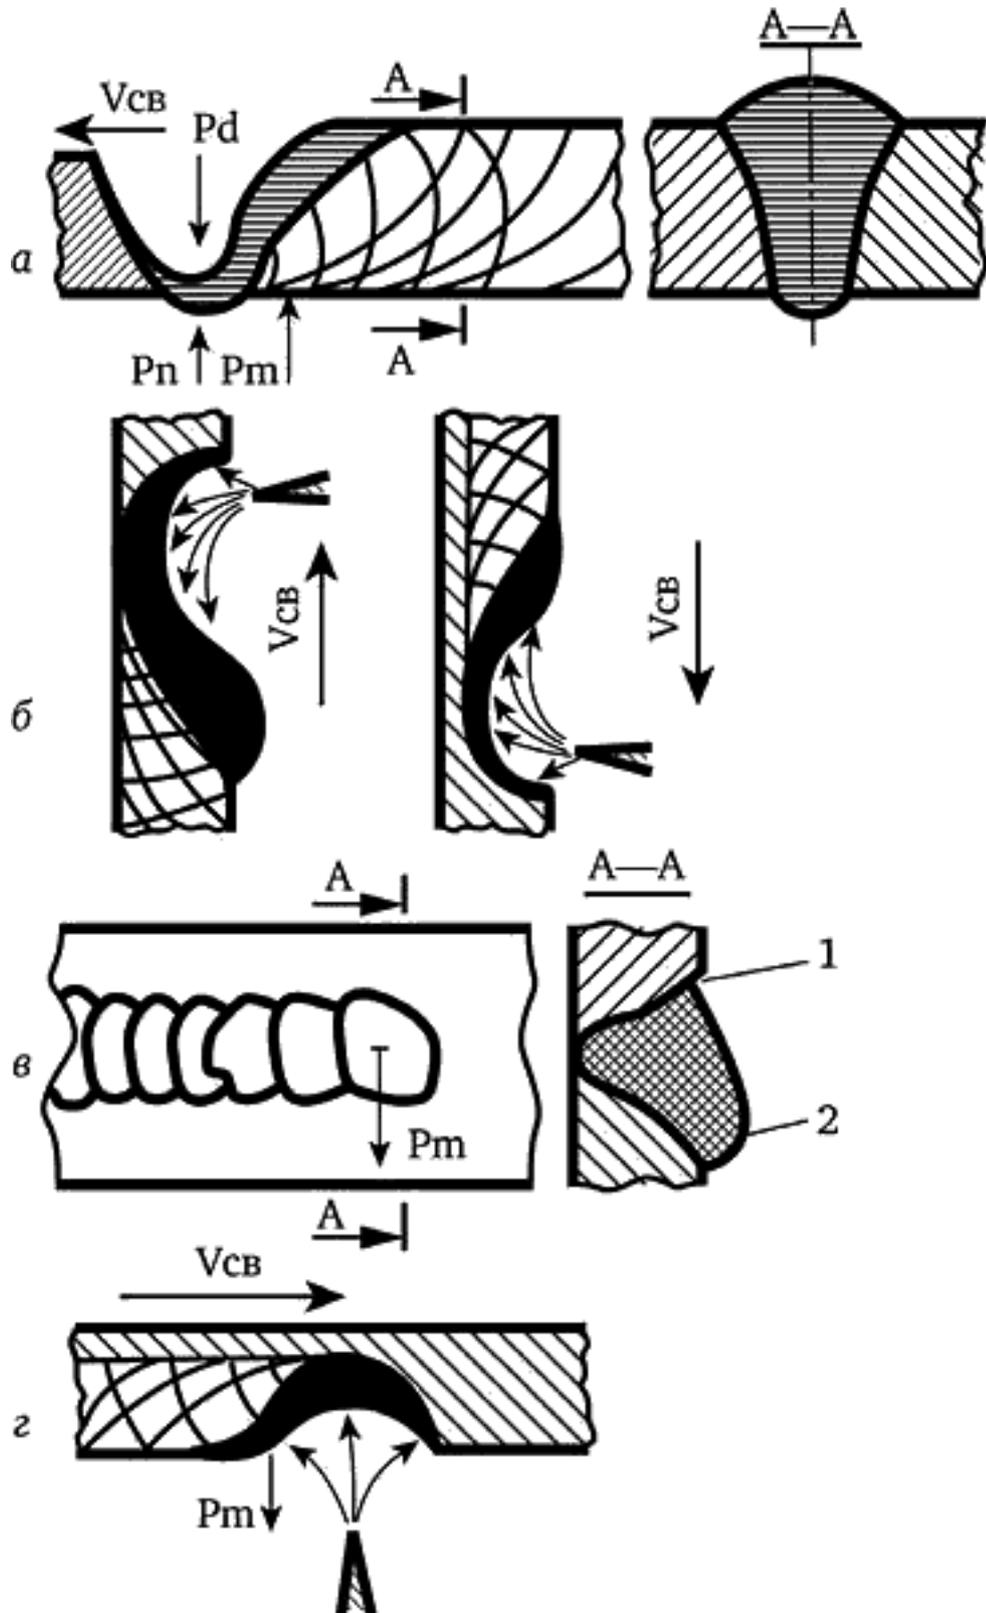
Силы, действующие в сварочной ванне, и формирование шва:
